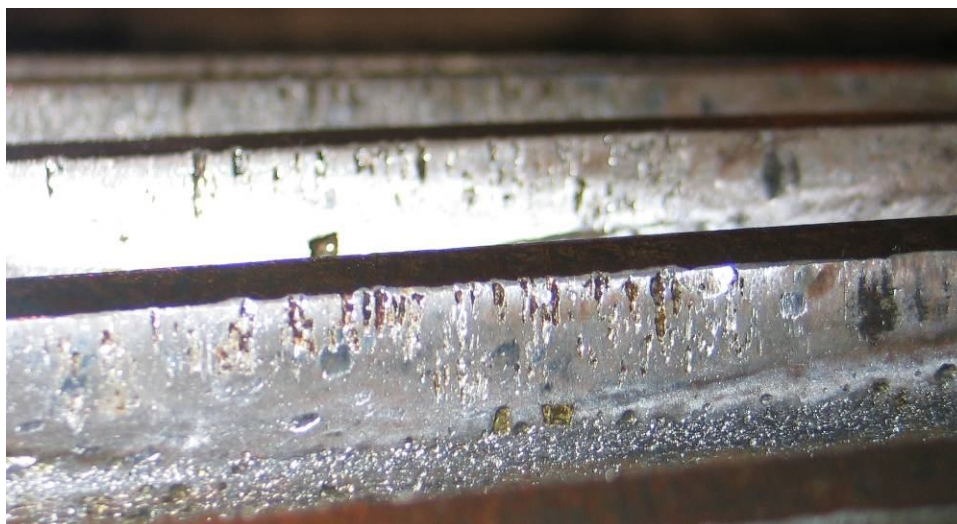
Вырывы металла на вершинах зубьев – схватывание поверхности при отсутствии разделительной масляной пленки
